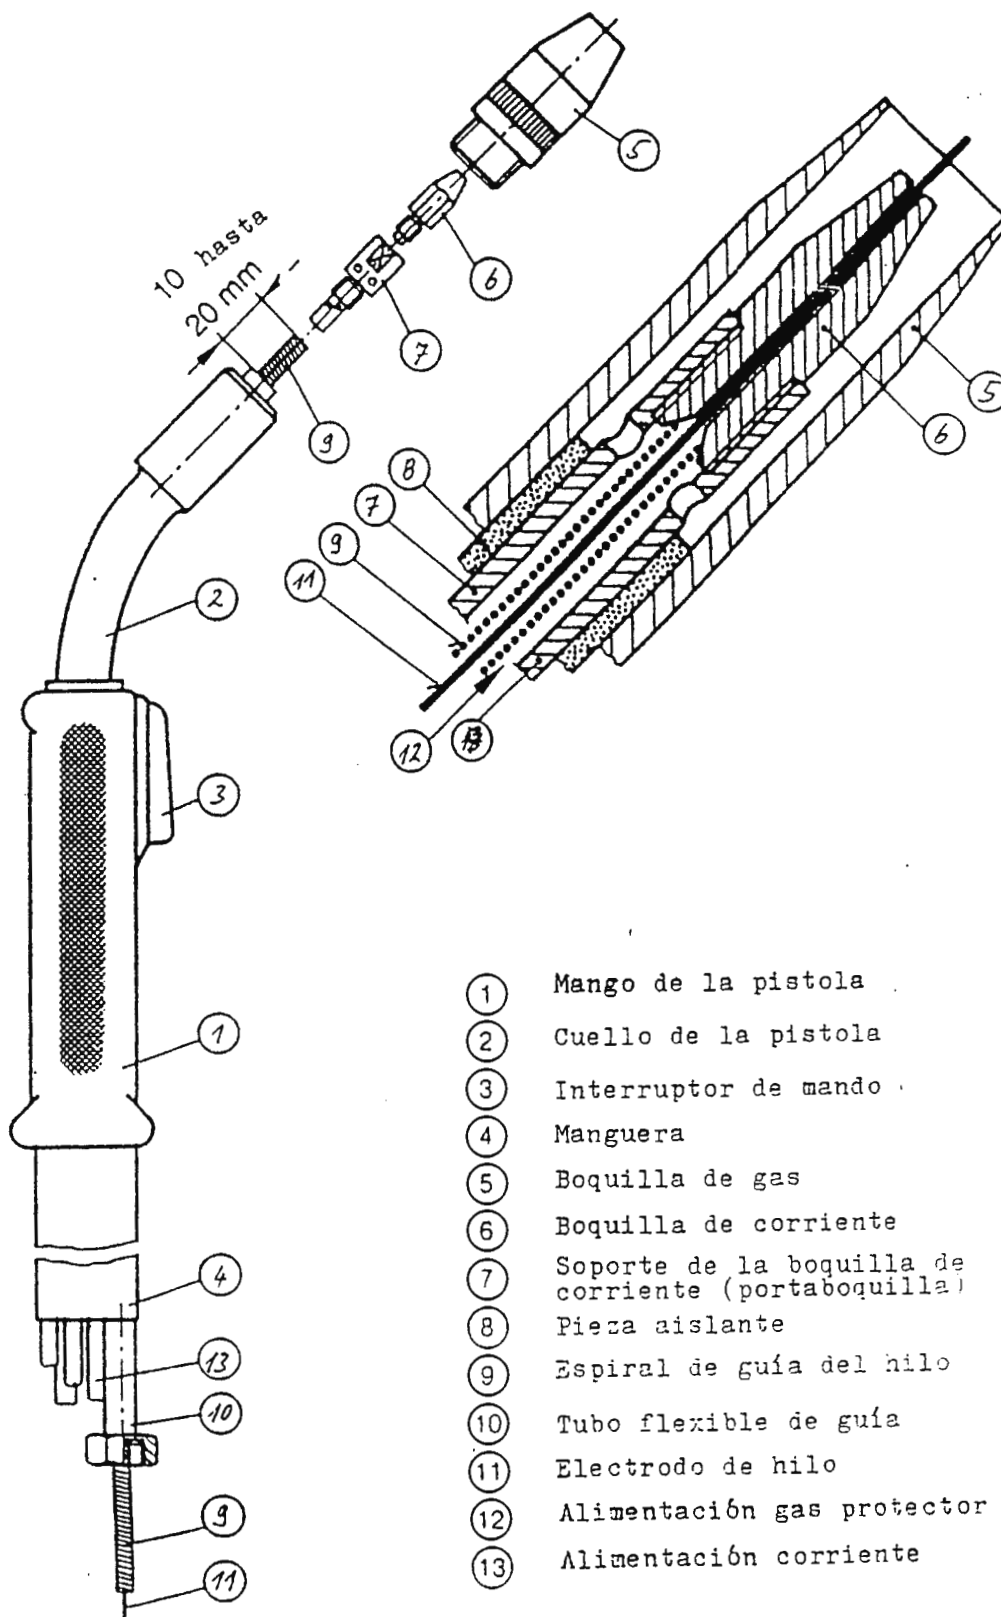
Esquema de pistola de soldadura M.I.G.
